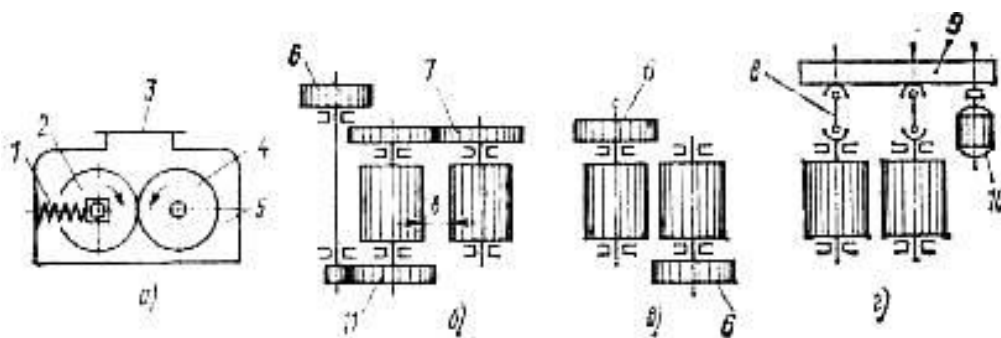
Схема двухвалковой дробилки (а) и привода валков (б—г) [3]
